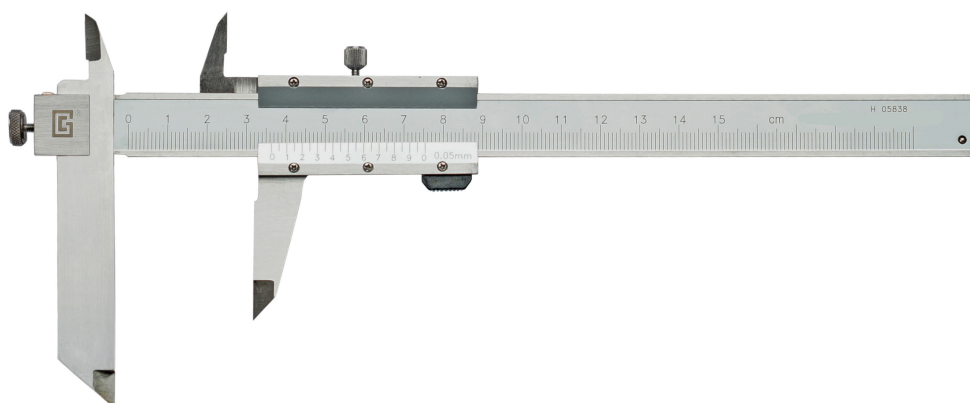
Общий вид штангенциркулей модели ШЦС-123
